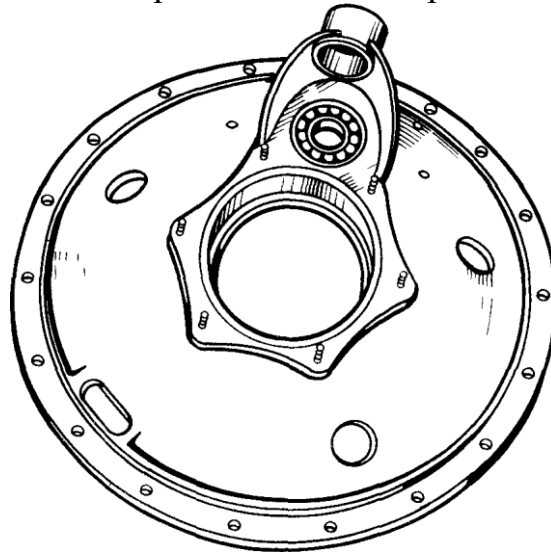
Передня кришка упорного шарикопідшипника колінчастого вала
